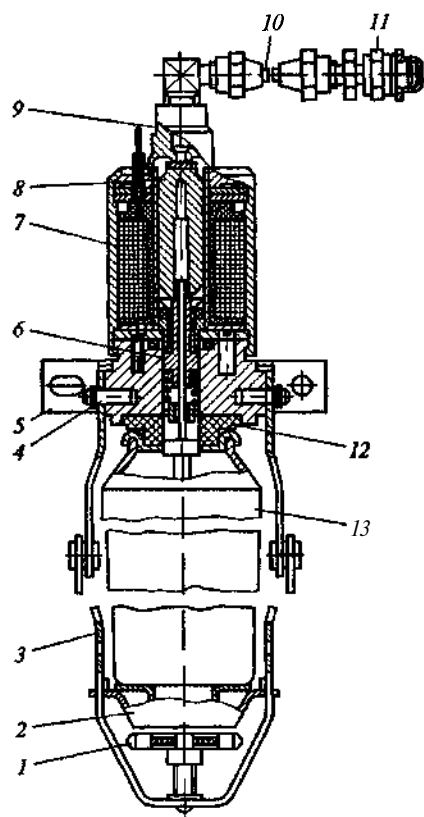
Электромагнитный привод аэрозольного пускового устройства: 1 — регулировочный винт; 2 — опорная пята; 3 — поводок; 4 — оси для установки поводков; 5 — кронштейн; 6 — эмульсионная трубка; 7 — электромагнит; 8 — якорь; 9 — пластинчатый клапан; 10 — трубопровод; 11 — форсунка; 12 — резиновая прокладка; 13 — аэрозольный баллон
